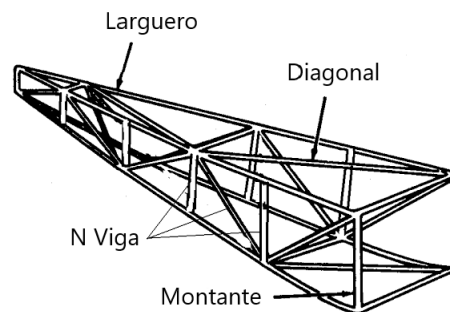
Fuselaje articulado Pratt. (U.N.L.P: Departamento de Aeronáutica, 2016).
